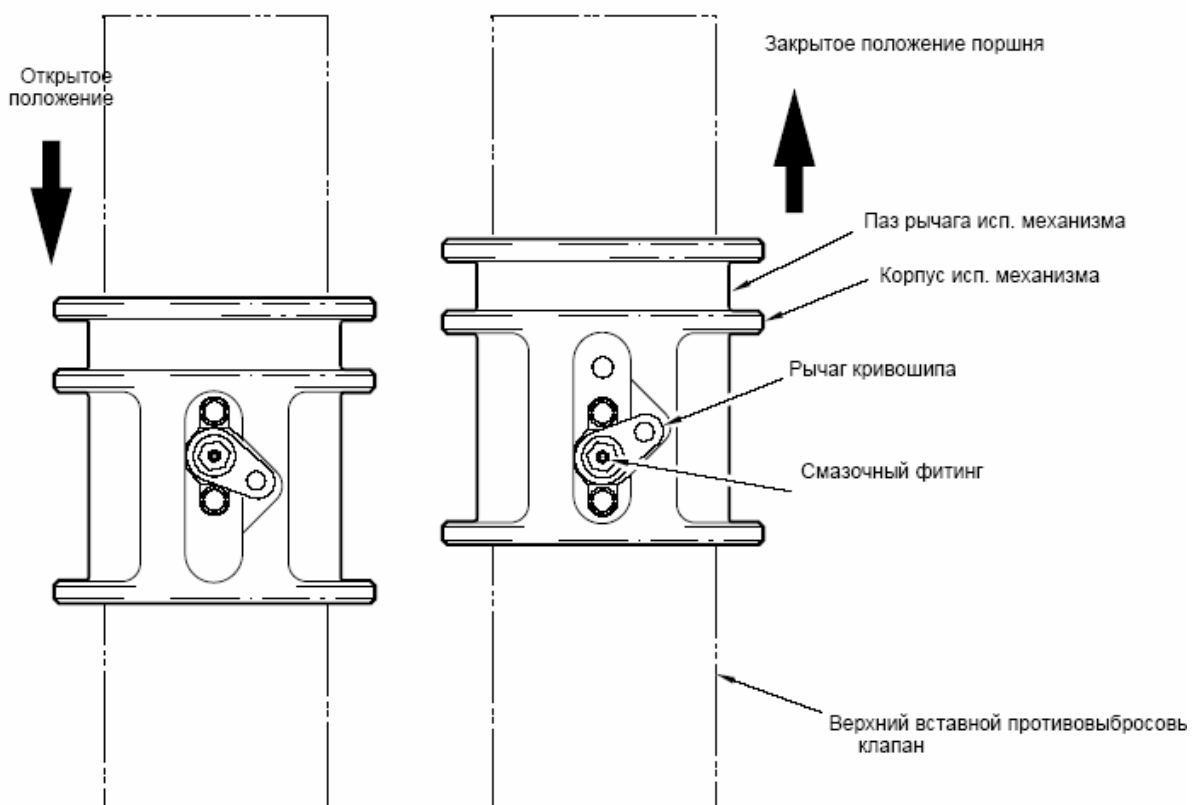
Смазка кривошипа исполнительного механизма предохранительного клапана
